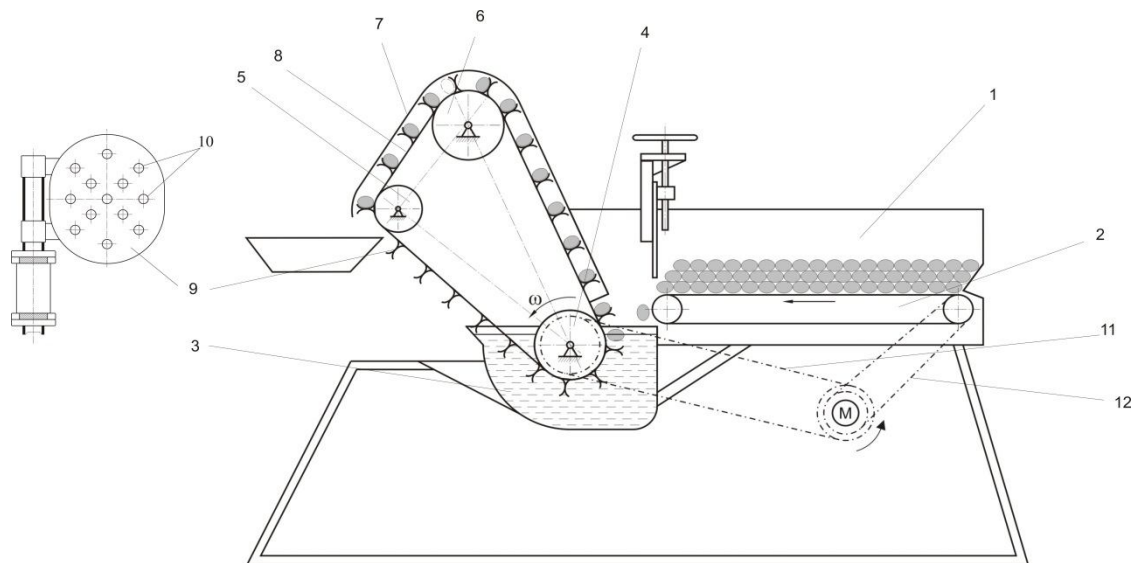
Принципиальная схема ложечно-ленточного высаживающего аппарата: 1 – бункер семенных клубней; 2 – донный транспортер; 3 – питательный ковш, 4 – ведущая звездочка; 5, 6, – ведомые звездочки; 7 – кожух; 8 – элеваторный транспортер; 9 – ложечка; 10 – дренажные отверстия; 11, 12 – цепная передача, 13 – электродвигатель, 14 – ограничитель.
